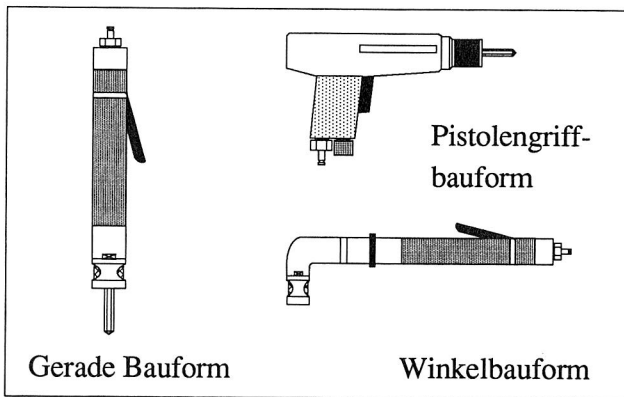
Bauformen typischer Schraubwerkzeuge
